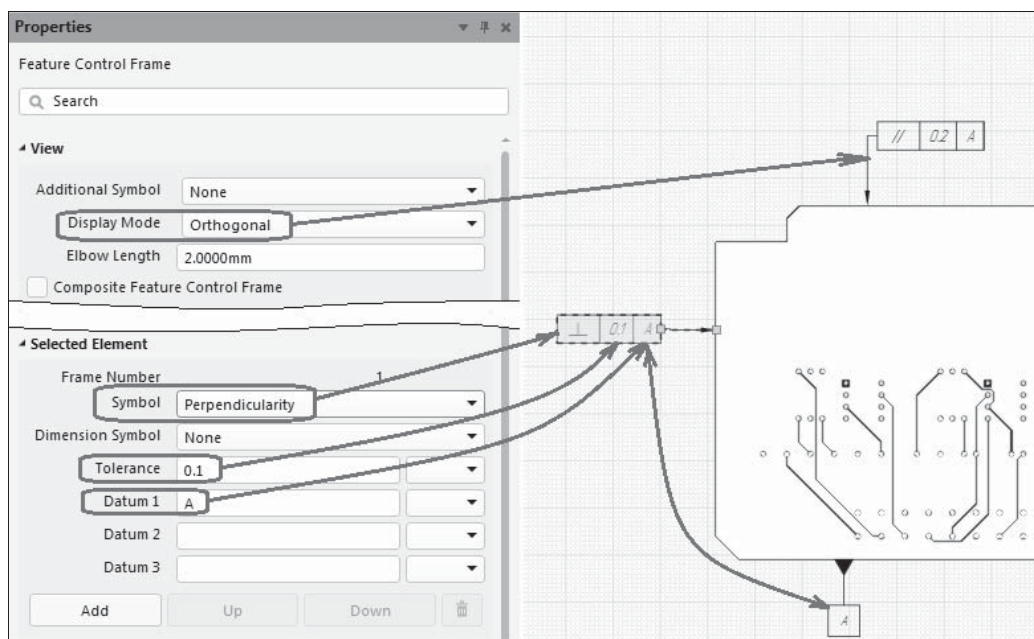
Обозначение баз и допусков формы и расположения поверхностей
